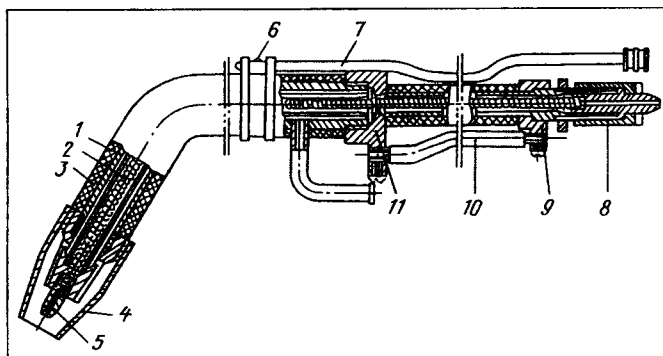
Шланговый держатель для полуавтоматической сварки: 1 — трубка горелки; 2 — спираль; 3 — резиновая оболочка; 4 — сопло; 5 — рукоятка; 6 — кнопка; 7 — шнур; 8 — токопровод; 9 и 11 — колодки; 10 — кабель
